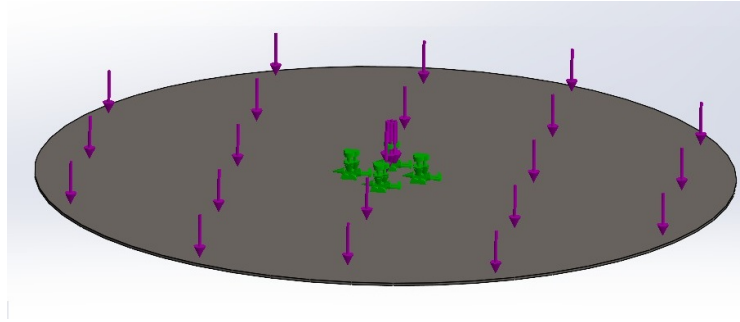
Placa de apoyo. Fuente: Autoría Propia
